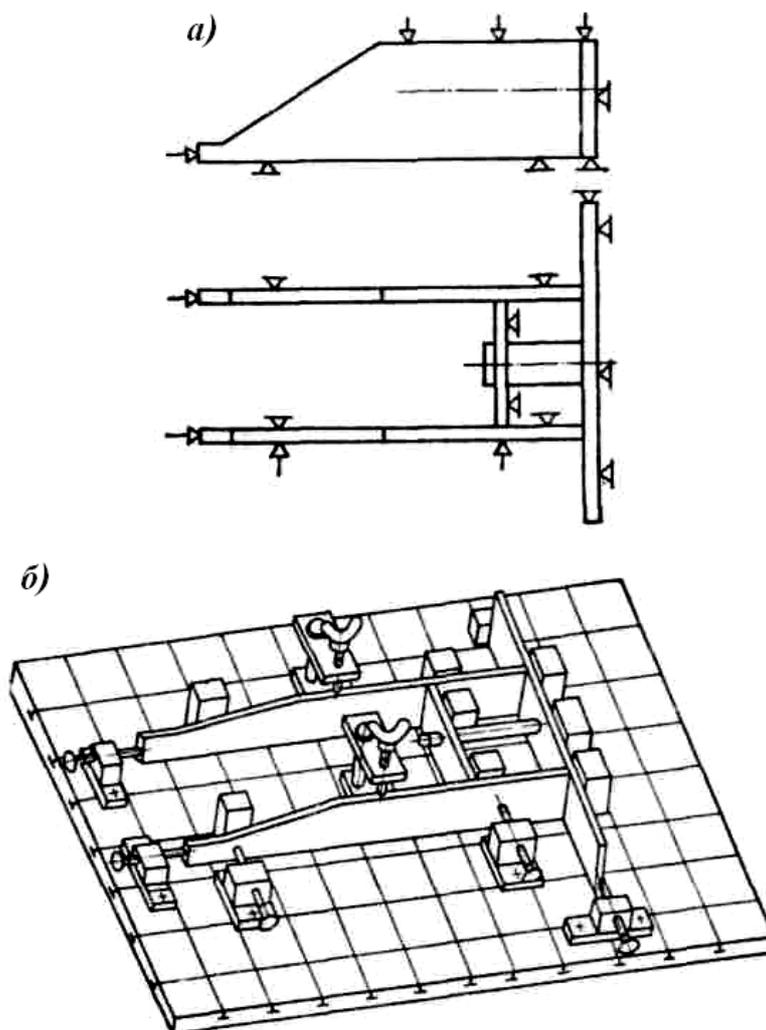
Принципиальная схема приспособления для сборки и сварки кронштейна (*а*) и общий вид УСПС (*б*)
